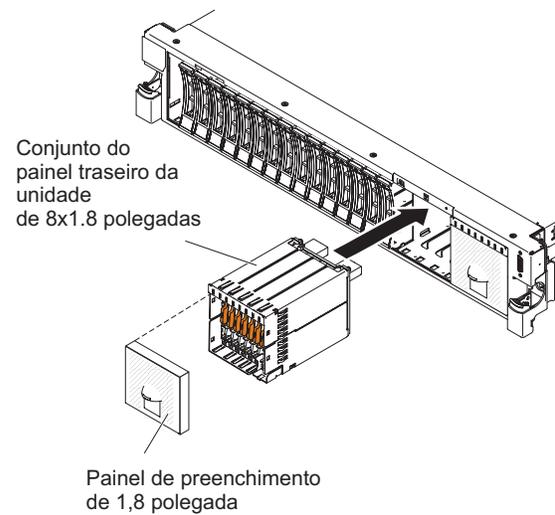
Instalação do Conjunto do Painel Traseiro de 1,8 Polegadas
